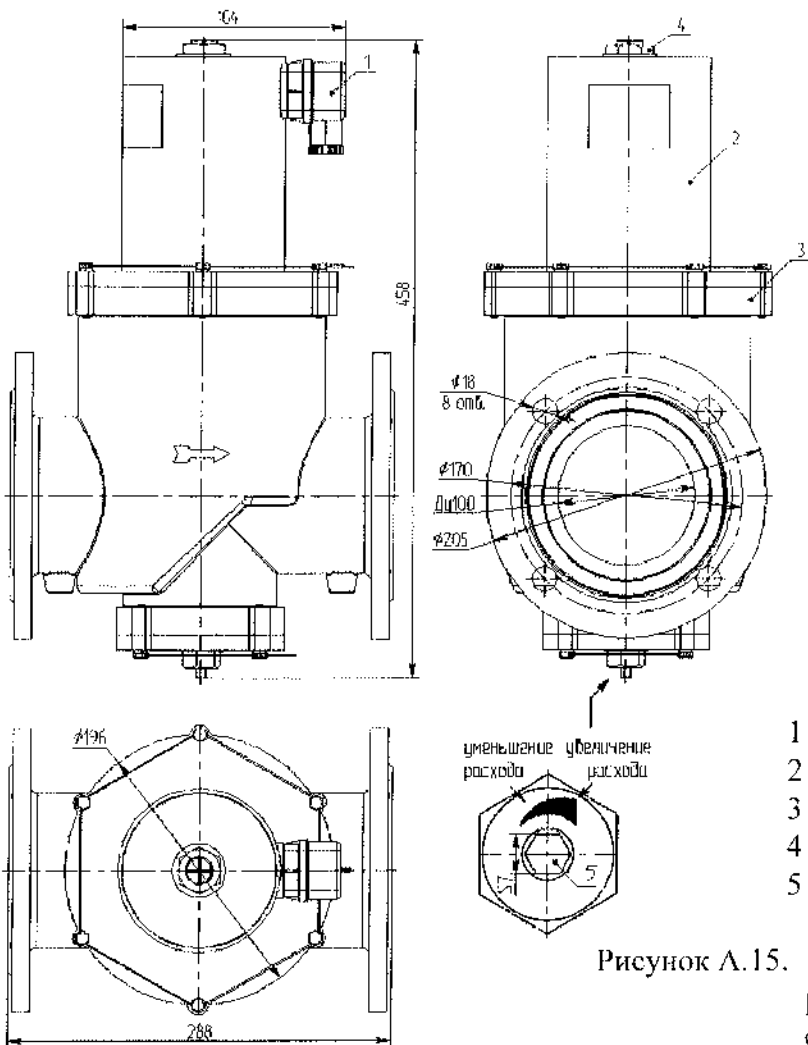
Габаритные и установочные размеры клапана КИ'ЭЗ-80 с регулировкой расхода
